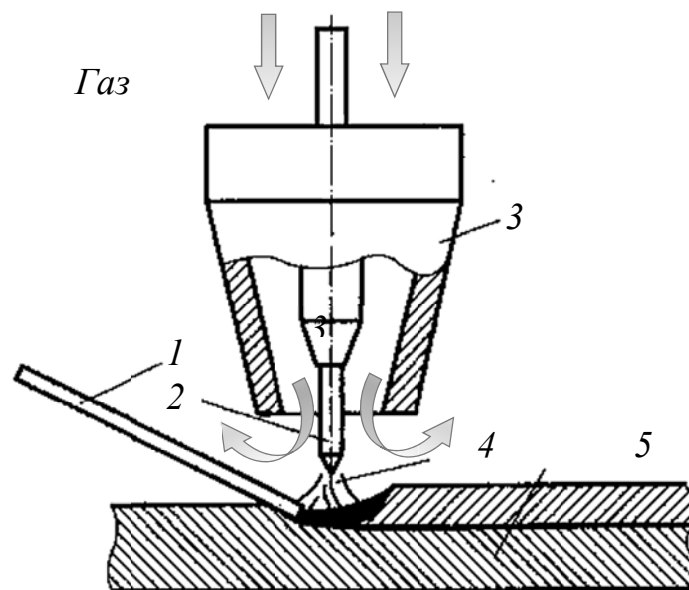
Схема дуговой сварки в среде защитных газов неплавящимся электродом:
